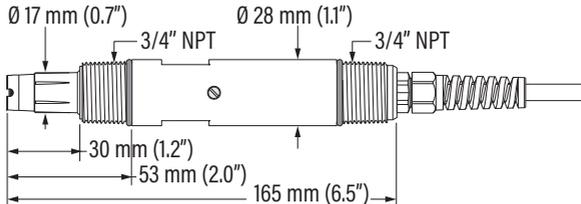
HI7640-18zz Sonda galvánica de OD con cable adjunto
